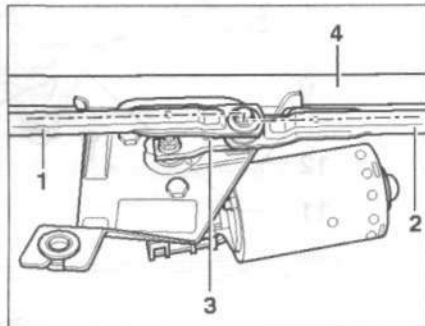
Ослабьте кривошип 3 и установите сначала соединительный рычаг 2, затем соединительный рычаг 1.
